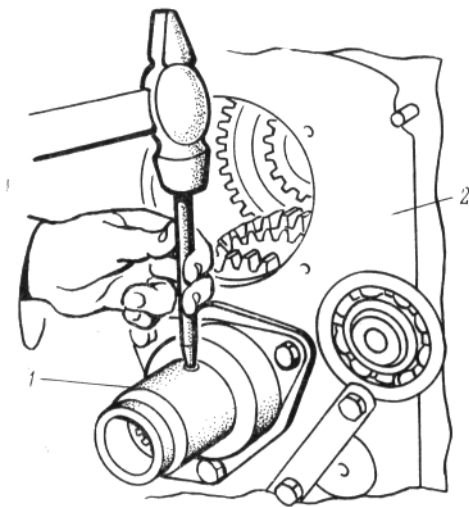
Випресування пружинного штифта внутрішнього вала: 1- гніздо внутрішнього вала; 2- корпус коробки передач
